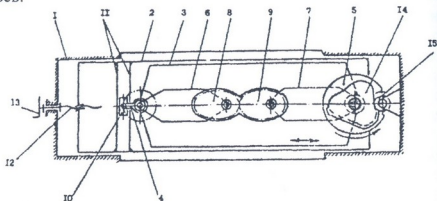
Схема устройства для обработки диаметральных кулачков: 1 – станина; 2 – салазки; 3 – каретка; 4 – задающий кривошип; 5 – поворотный стол; 6, 7 – редукторы; 8, 9 – некруглые колеса; 10 – камень; 11 – направляющие; 12 – винтовая пара; 13 – маховик; 14 – заготовка; 15 – фреза
